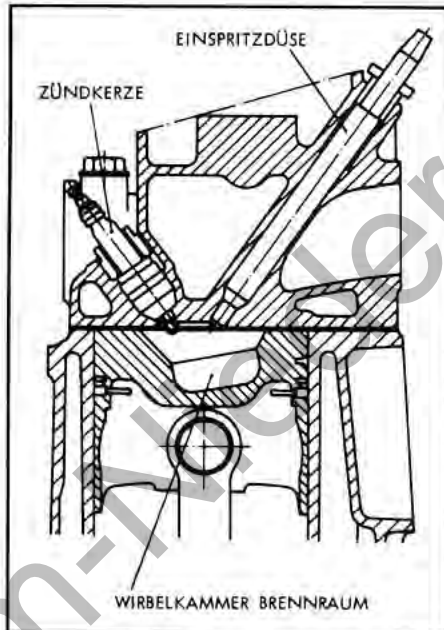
Schichtlademotor mit Wirbelkammer.
